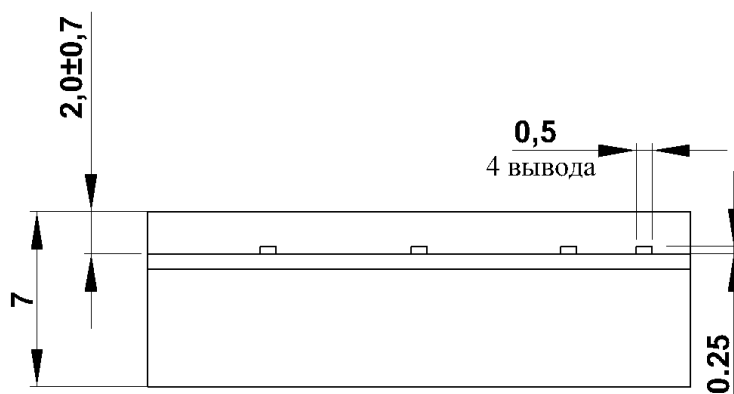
Габаритный чертеж модулей в корпусе «Н»
